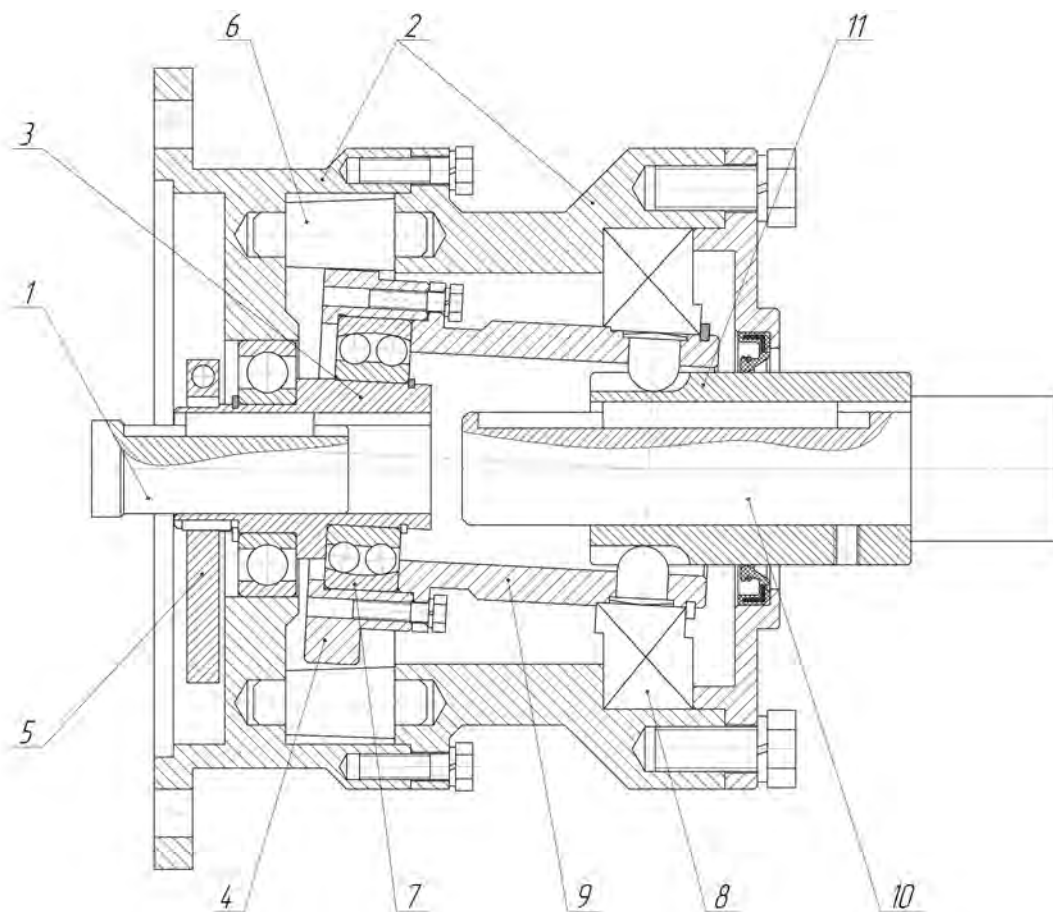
Общий вид мотор-редуктора на базе ППП типа К-Н-V с передаточным отношением 15
